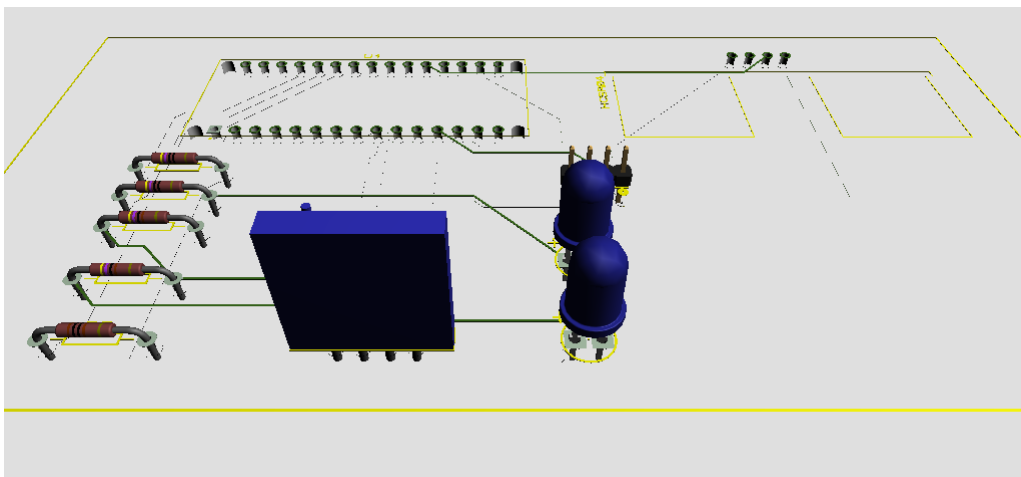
Vista 3D del resultado de la tarjeta PCB impresa
